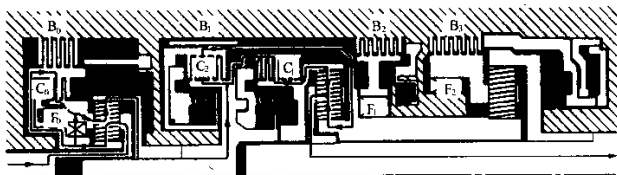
3档齿轮 (换档杆置D或2位置) 传动结构简图
